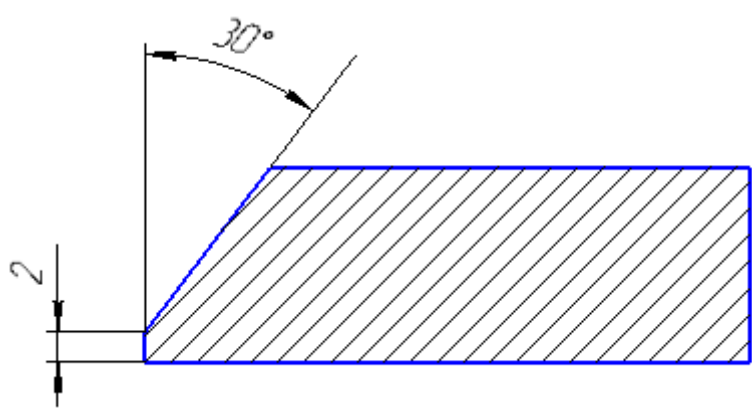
Конструктивный элемент подготовленных кромок свариваемых деталей
